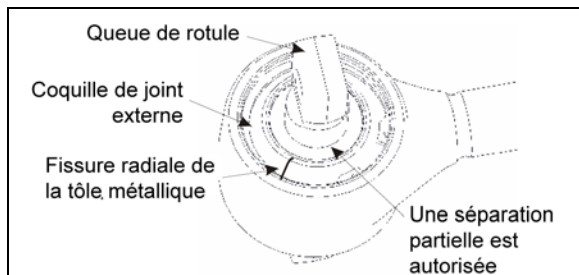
BAGUE DE QUEUE DE ROTULE
